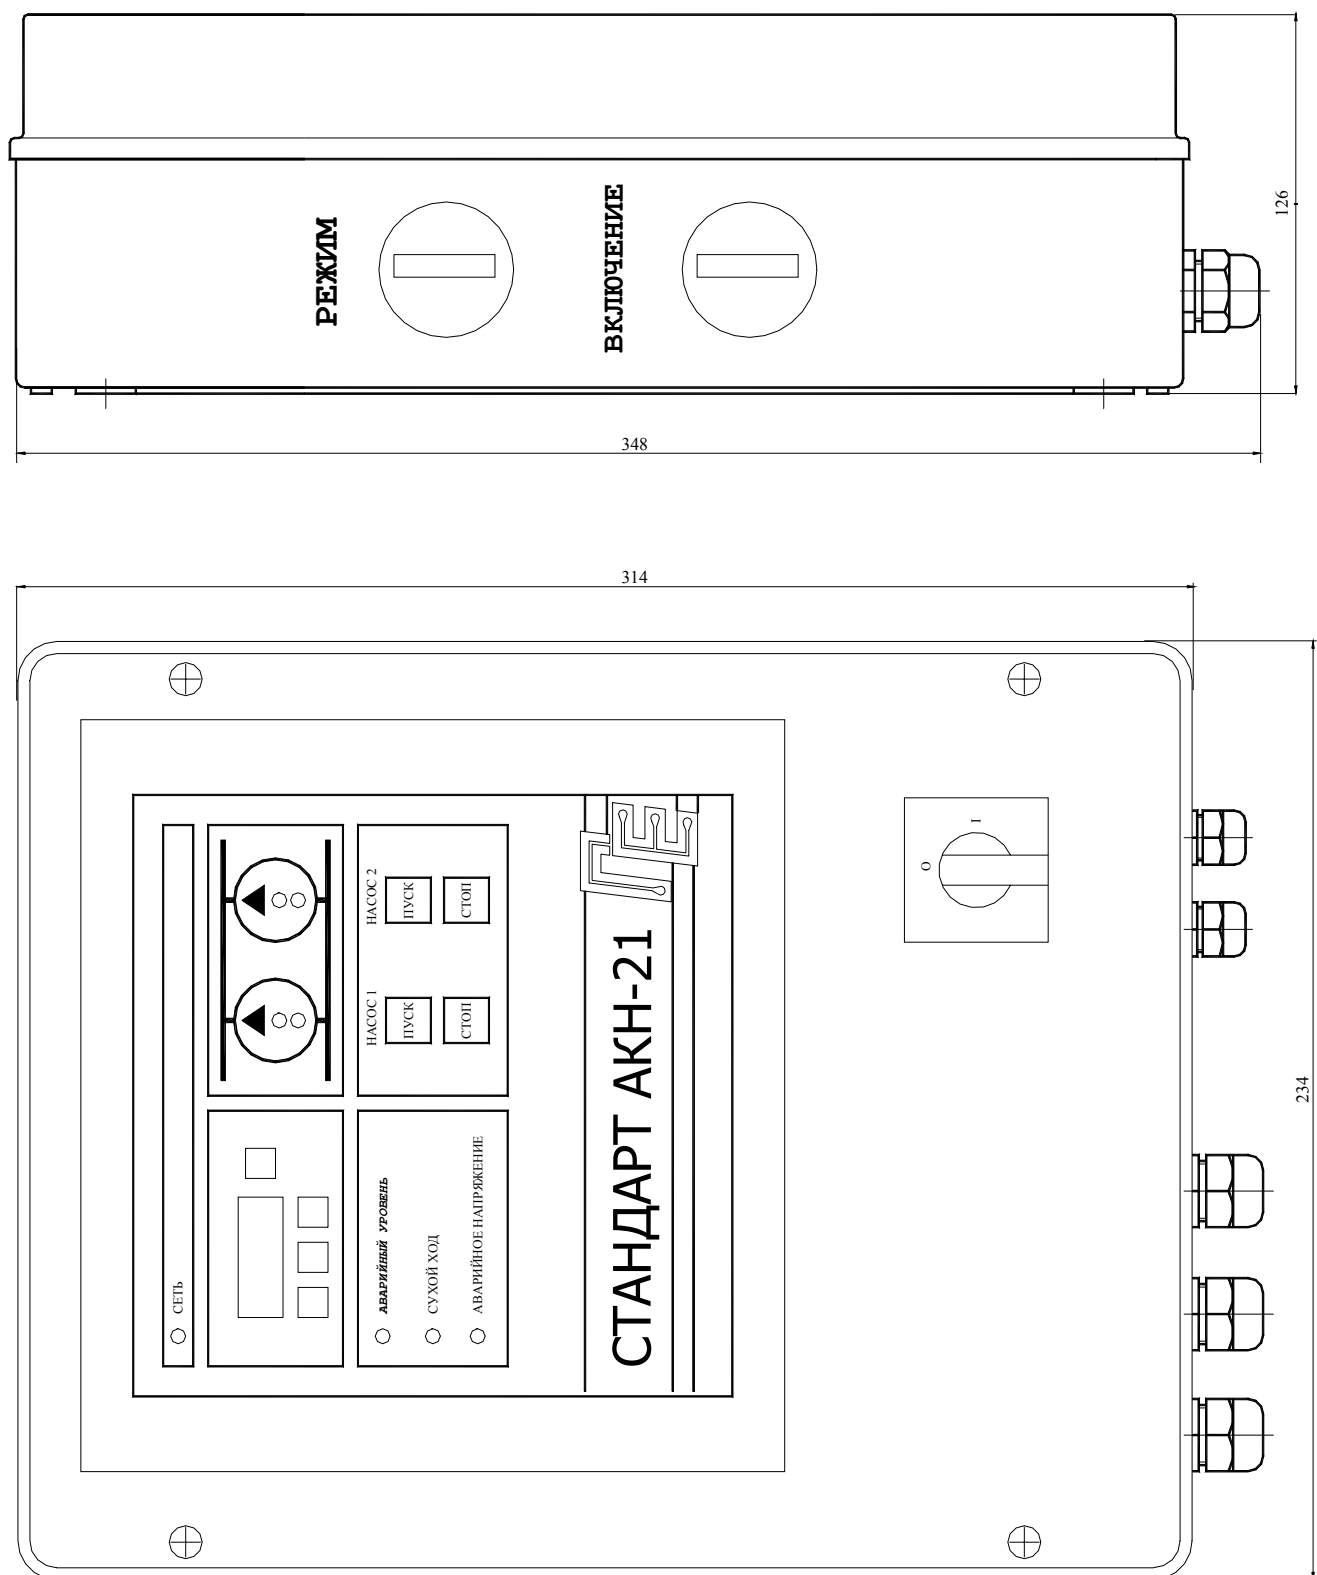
Общий вид устройства СТАНДАРТ АКН-21Д
